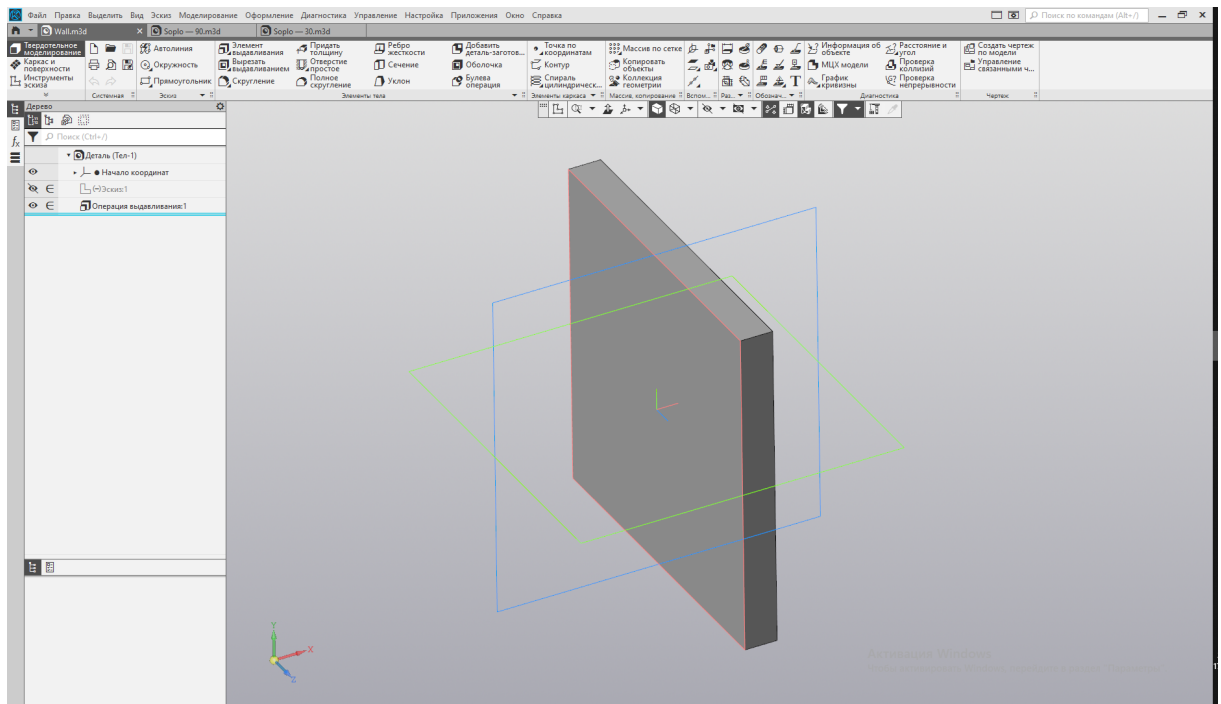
Компас 3D – 3D-модель обрабатываемой поверхности
